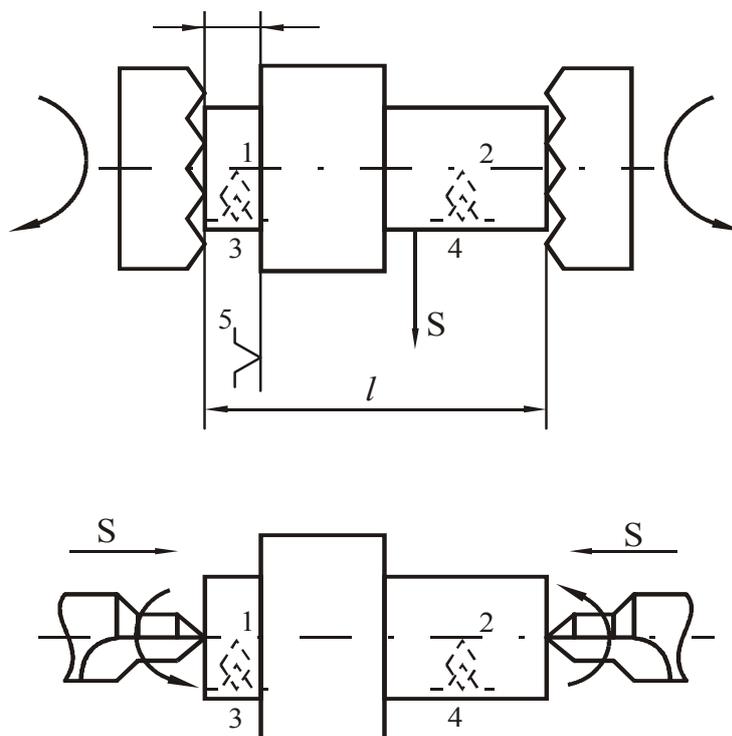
Схема выполнения фрезерно-центровальной операции
